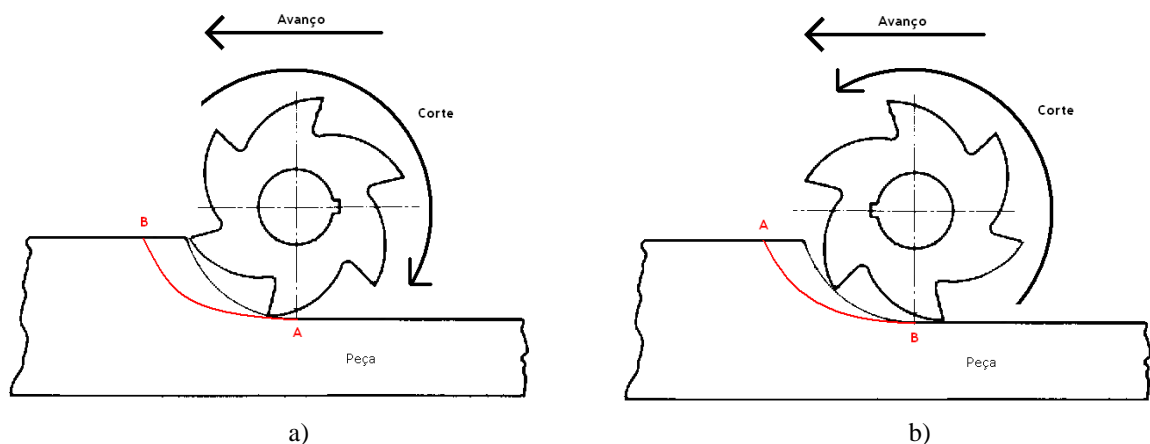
Fresagem cilíndrica discordante (a) e concordante (b).
